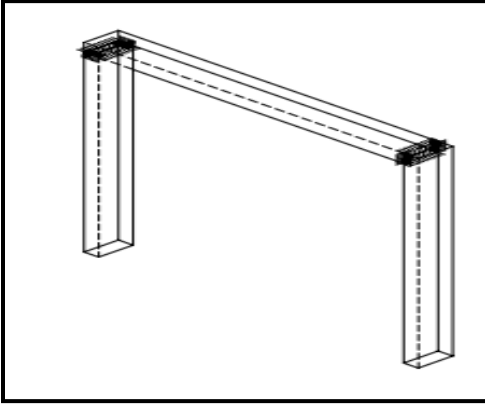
Indicación de soldadura en la pieza, MBC-C-15-3.
